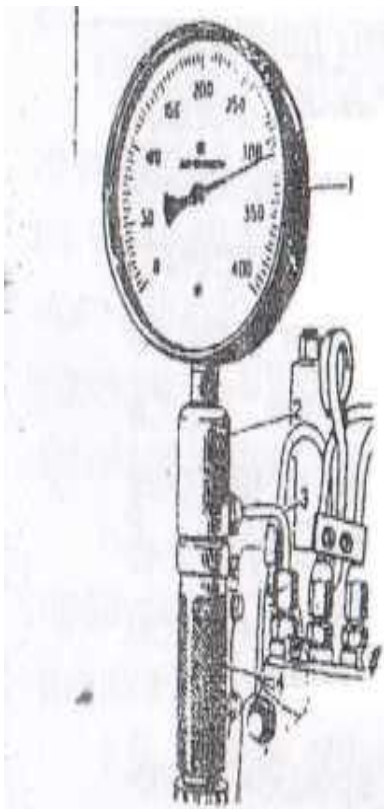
Проверка изношенности плунжерной пары приспособлением КИ-4802: 1- манометр; 2 – корпус приспособления; 3 – топливопровод; 4 – рукоятка.
